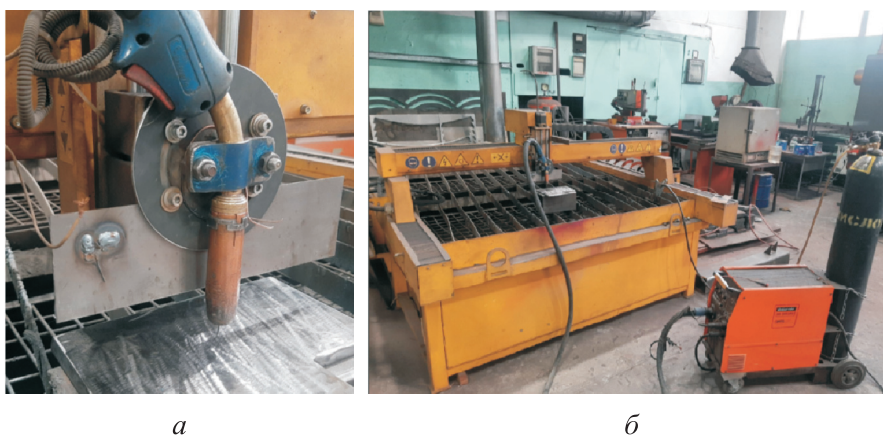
Внешний вид кронштейна крепления сварочной горелки (а) и комплектации станка для ДАН (б)
